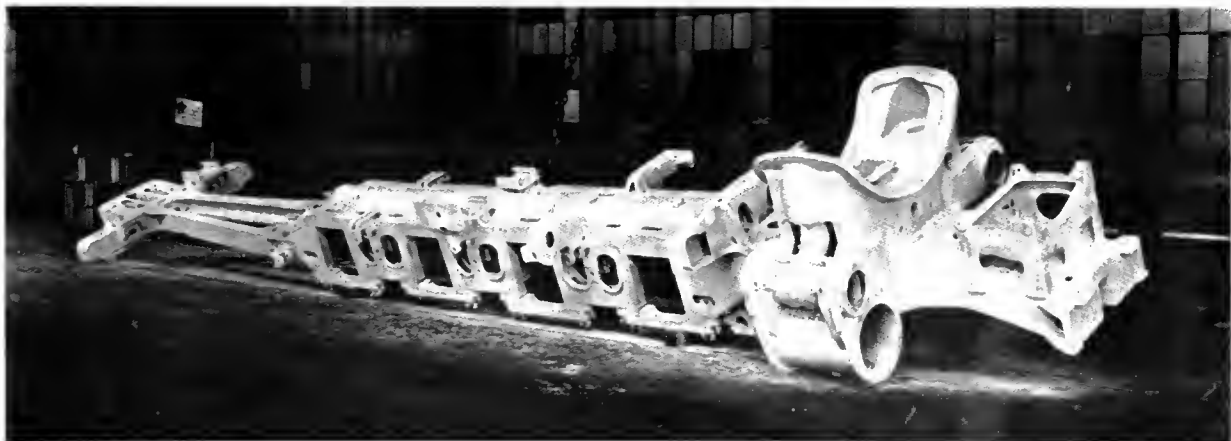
Châssis monobloc en acier moulé de locomotive Delaware et Hudson 4-8-4 (S.N.C.F.)
